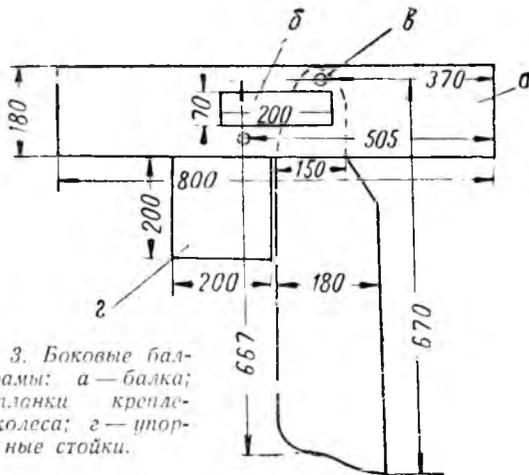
Боковые балки рамы: а — балка; б — планки крепления колеса; в — упорные стойки.
